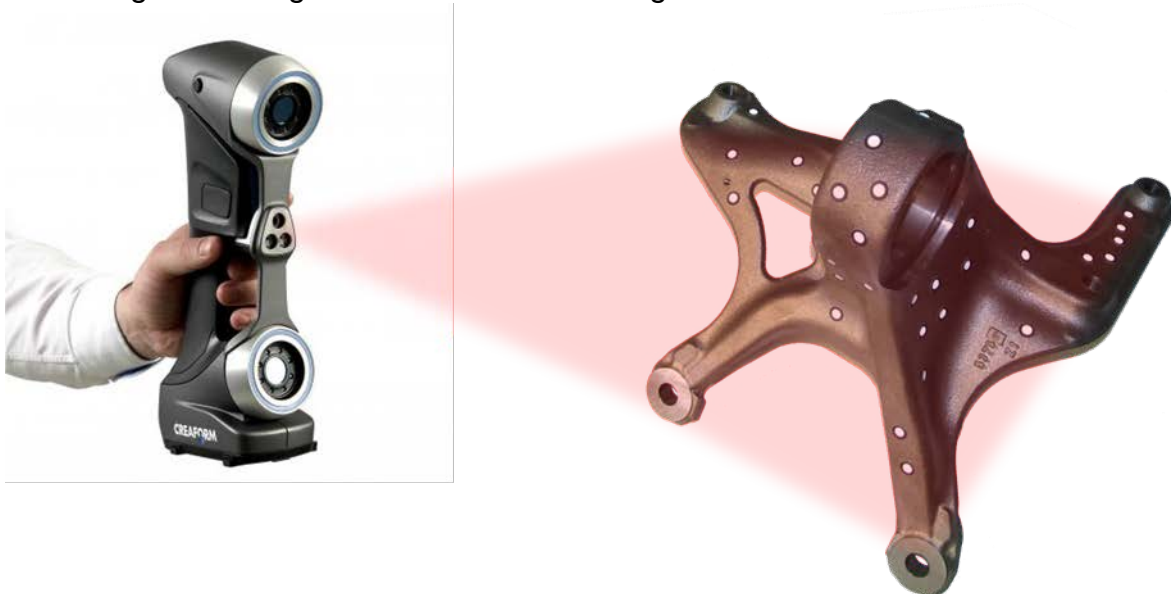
Handgeführter 3D-Laserscanner – Prinzipskizze
